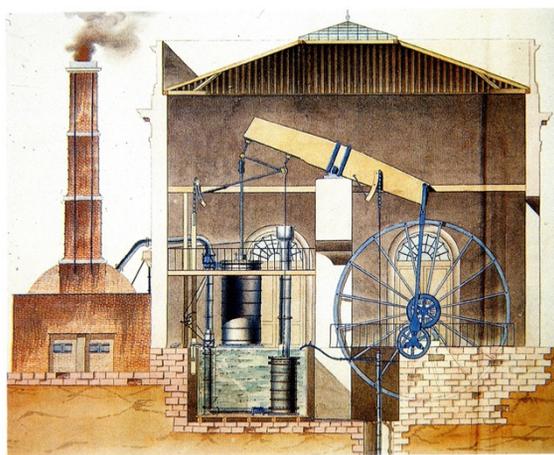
Machine à vapeur de Watt, version Agustín de Betancourt (c. 1788).
